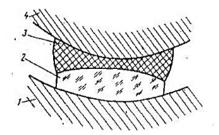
Эластичное крепление I – приспособление, 2 – линза, 3 – смоляная пробка, 4 – инструмент
